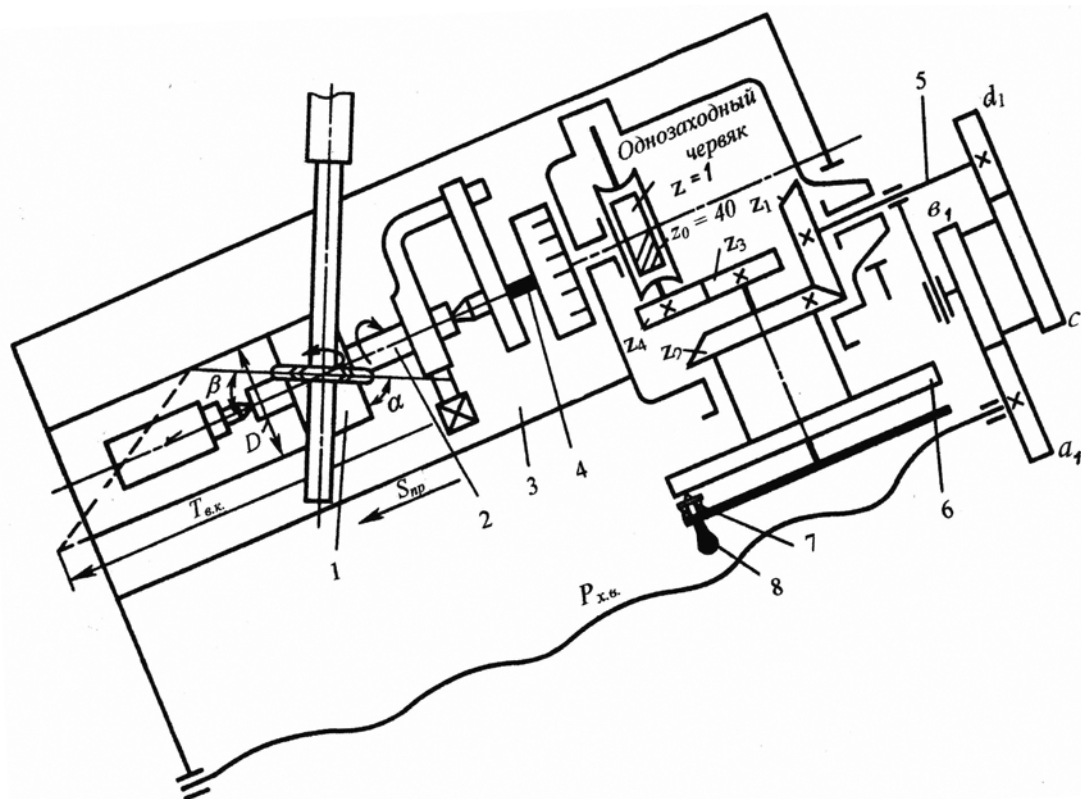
Схема наладки универсально-фрезерного станка и делительной головки на фрезерование винтовых канавок
